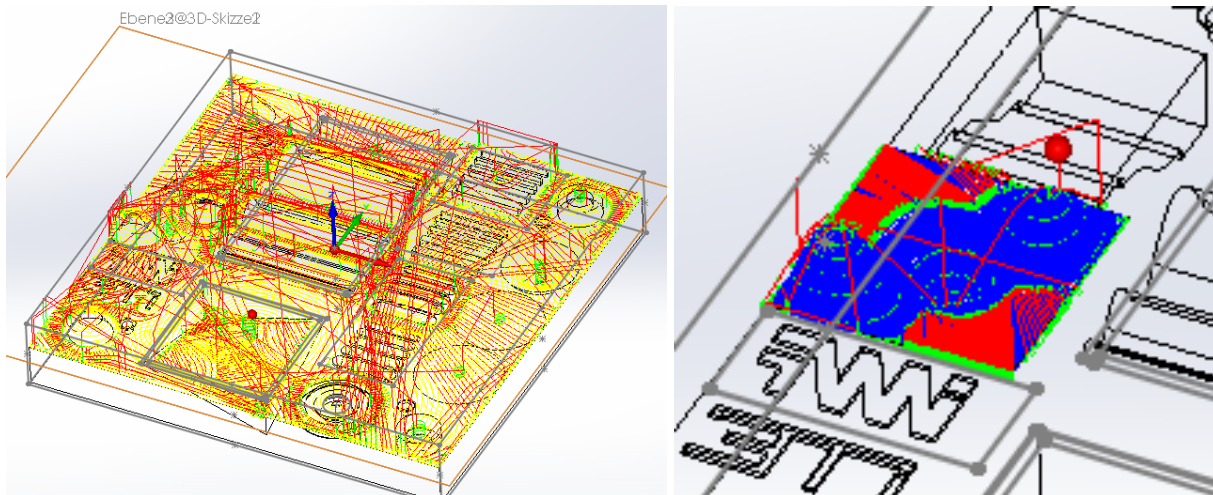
Beispiel Fräsbahnplanung Wachsschaltafel Block A: Schruppbearbeitung mit Schafffräser  $d = 16 \text{ mm}$ ,  $n = 9776 \text{ U/min}$ ,  $v_f = 5024 \text{ mm/min}$  (links); Kopierfräser (Vollradiusfräser)  $d = 7 \text{ mm}$ ,  $n = 10004 \text{ U/min}$ ,  $v_f = 1120 \text{ mm/min}$  für die Bearbeitung der stark gekrümmten Freiformfläche des Formenbausteins Nr. 7.2 (rechts)
